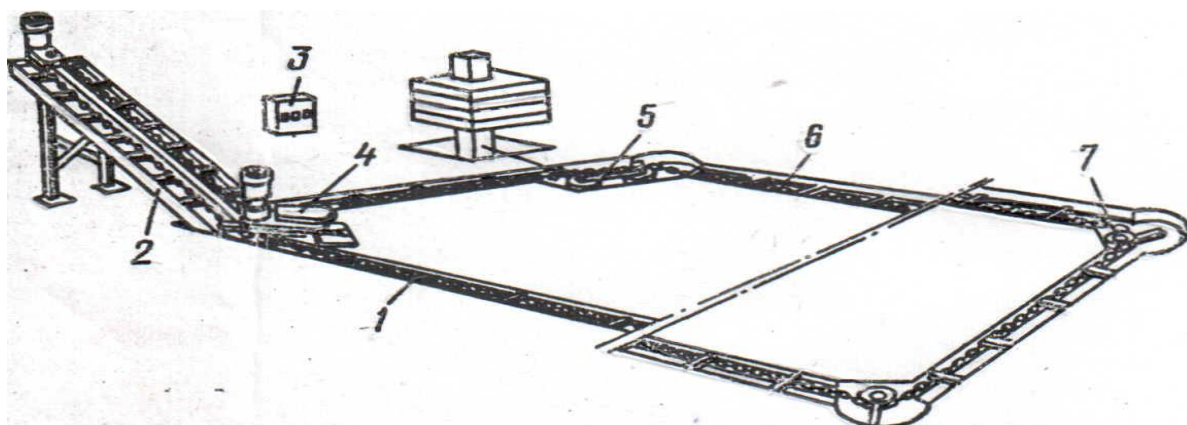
Транспортёр скребковый навозоуборочный ТСН-160:
